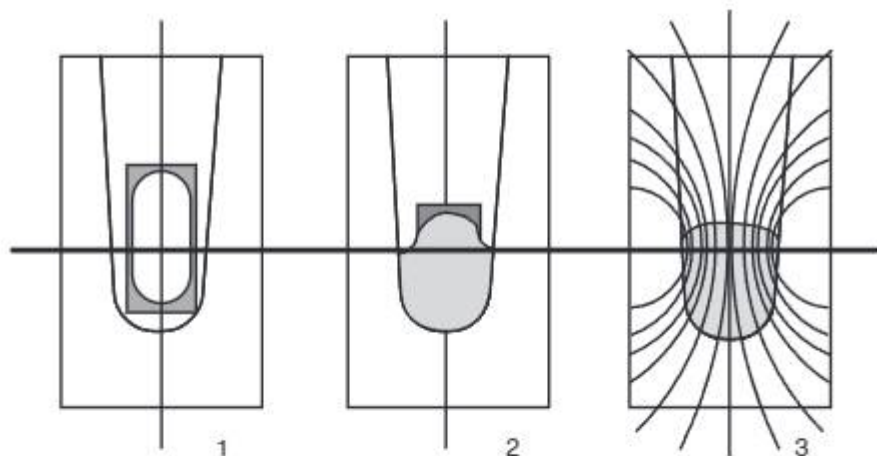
Механизм расплавления металла: 1 — заготовка после включения нагрева токами высокой частоты в индуктор в течение нескольких секунд нагревается по поверхности до температуры 900–1000 °С, грани заготовки нагреваются выше примерно на 100 °С; 2 — плавка заготовки начинается снизу, так как дно тигля создает условия для меньших теплотерь; заготовка начинает погружаться и постепенно тонет в жидком металле, повышая его уровень в тигле; 3 — образуется расплавленный металл с выпуклым мениском и тонкой пленкой окислов на поверхности. При повышении температуры металла до 1550–1600 °С его жидкотекучесть достигает состояния, при котором поле токов высокой частоты, имеющее вихревой характер, перемешивает жидкий металл и разрывает окисную пленку, сигнализируя, что надо выключить нагрев токами высокой частоты, так как металл готов для заливки форм
